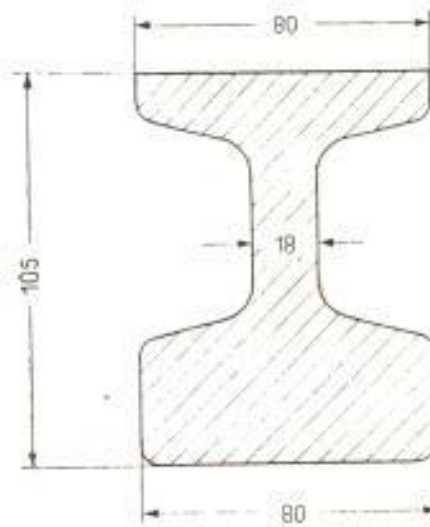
PERFIL Y DIMENSIONES (MM)
